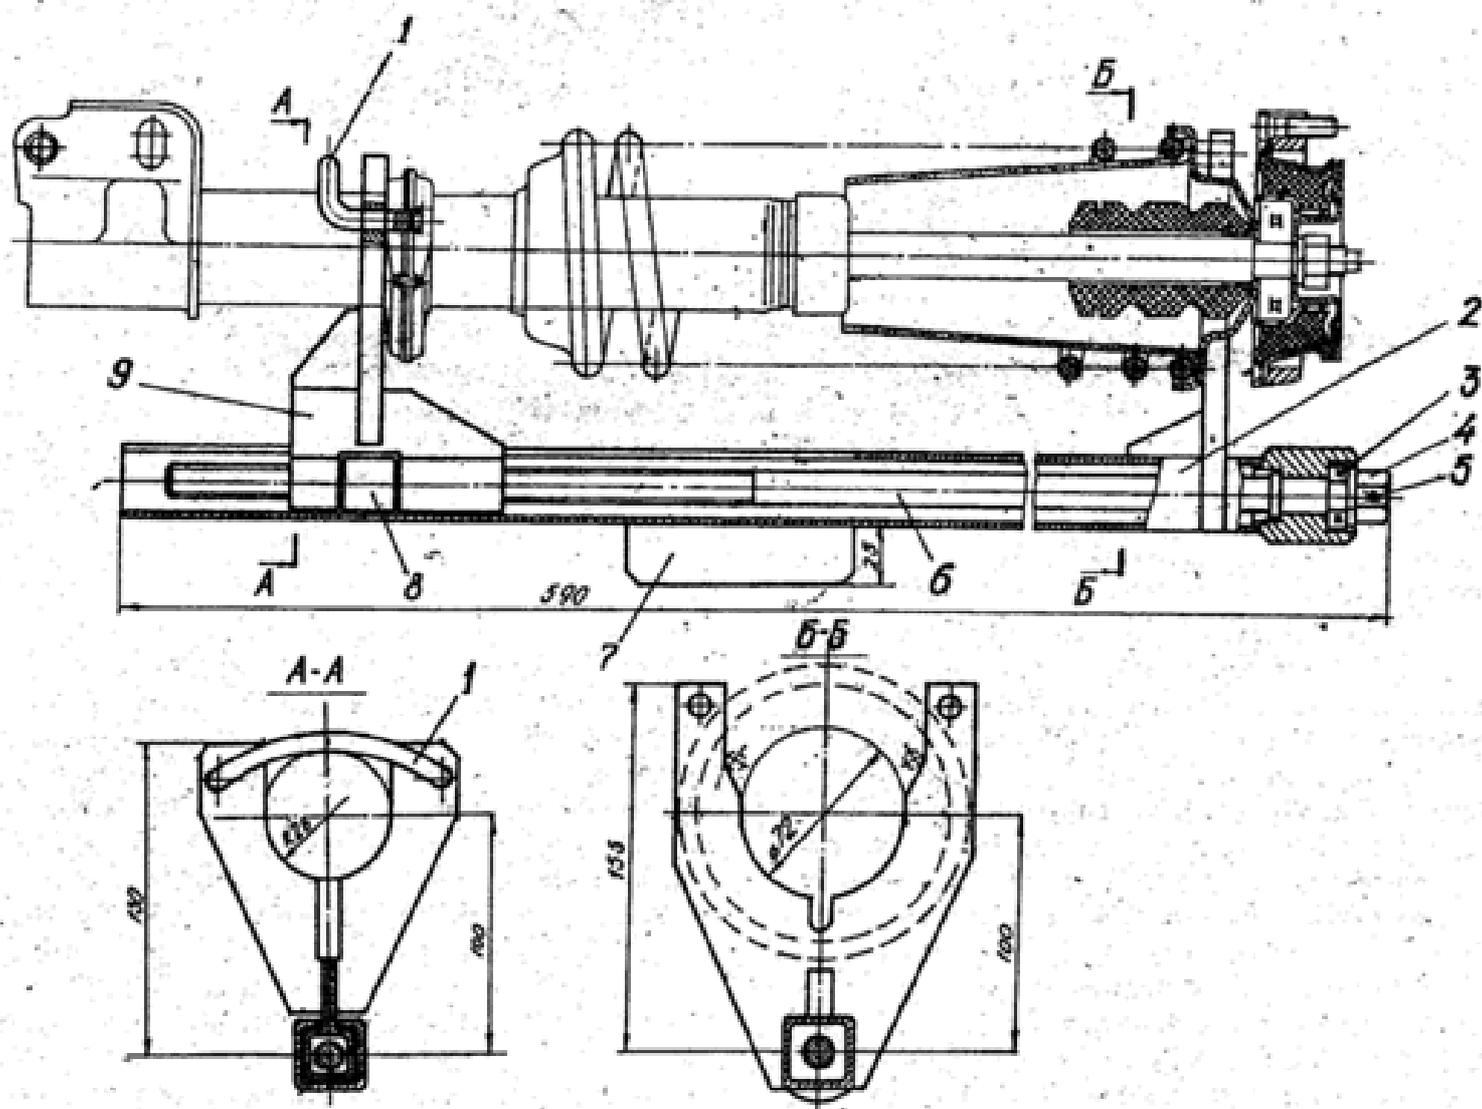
Приспособление М9832-559 для сборки и разборки стойки передней подвески: 1 - скоба; 2 - корпус в сборе; 3 - подшипник; 4 - гайка; 5 - штифт; 6 - винт несущий; 7 - фланец; 8 - гайка; 9 - суппорт в сборе.
